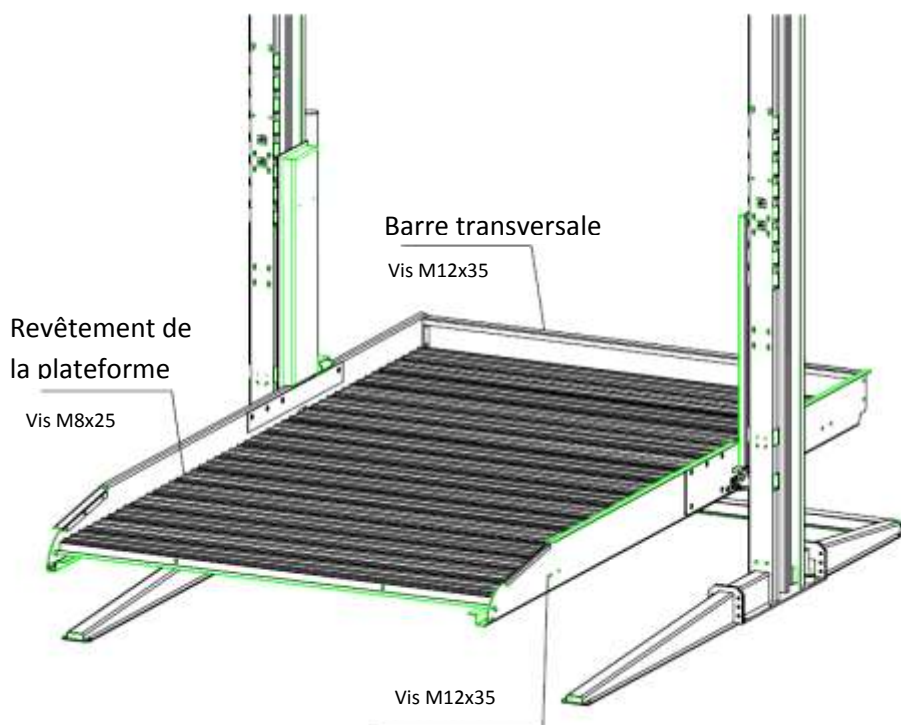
Montage du revêtement de la plateforme et de la barre transversale de la plateforme
